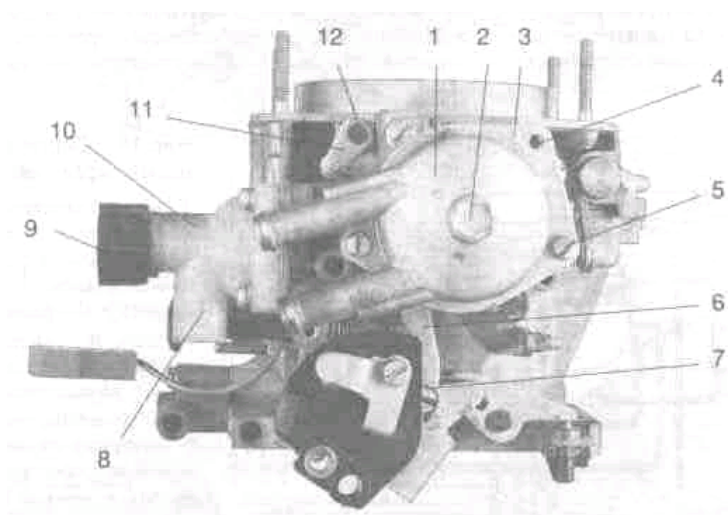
Вид на карбюратор 21083-1107010-62 со стороны автоматического пускового устройства
